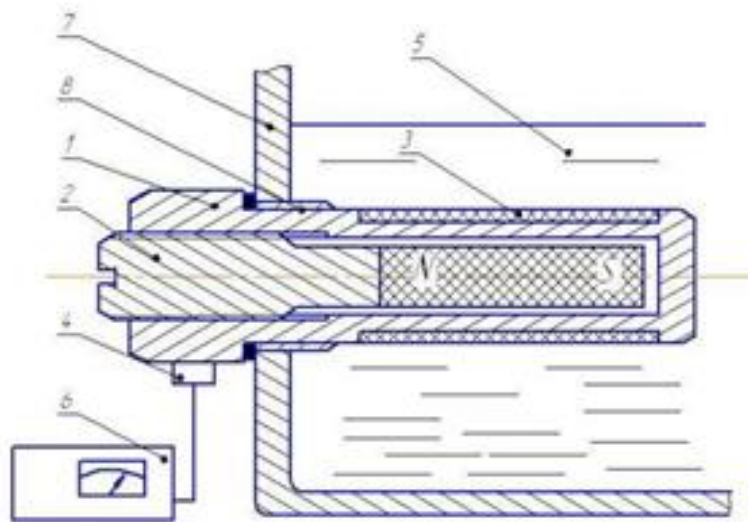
Датчик: 1 – корпус датчика; 2 – магнітний сердечник; 3 – чутливий елемент; 4 – електричний роз'єм; 5 – мастило; 6 – реєструючий прилад; 7 – корпус редуктора; 8 – різьбове з'єднання [57]
